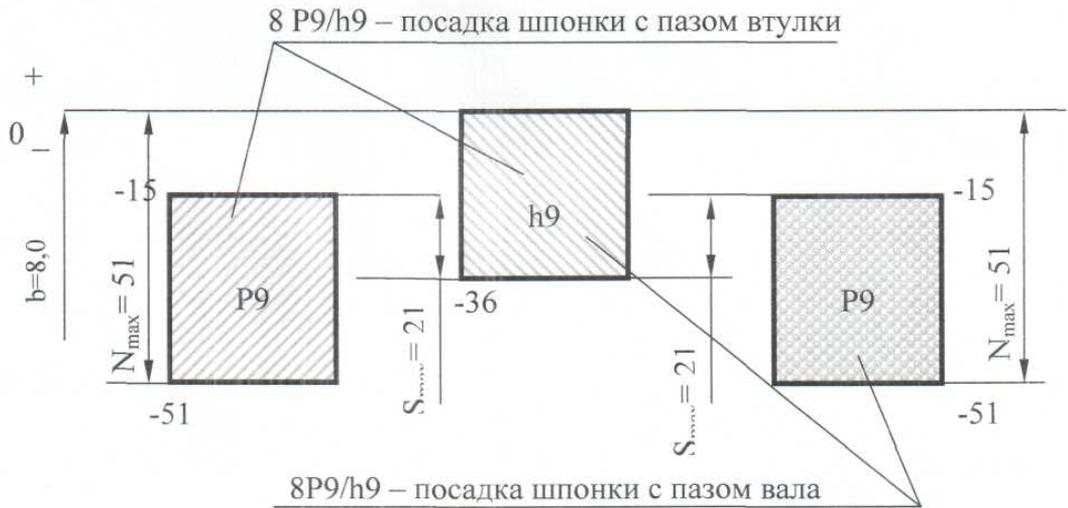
Схема полей допусков шпоночного соединения
